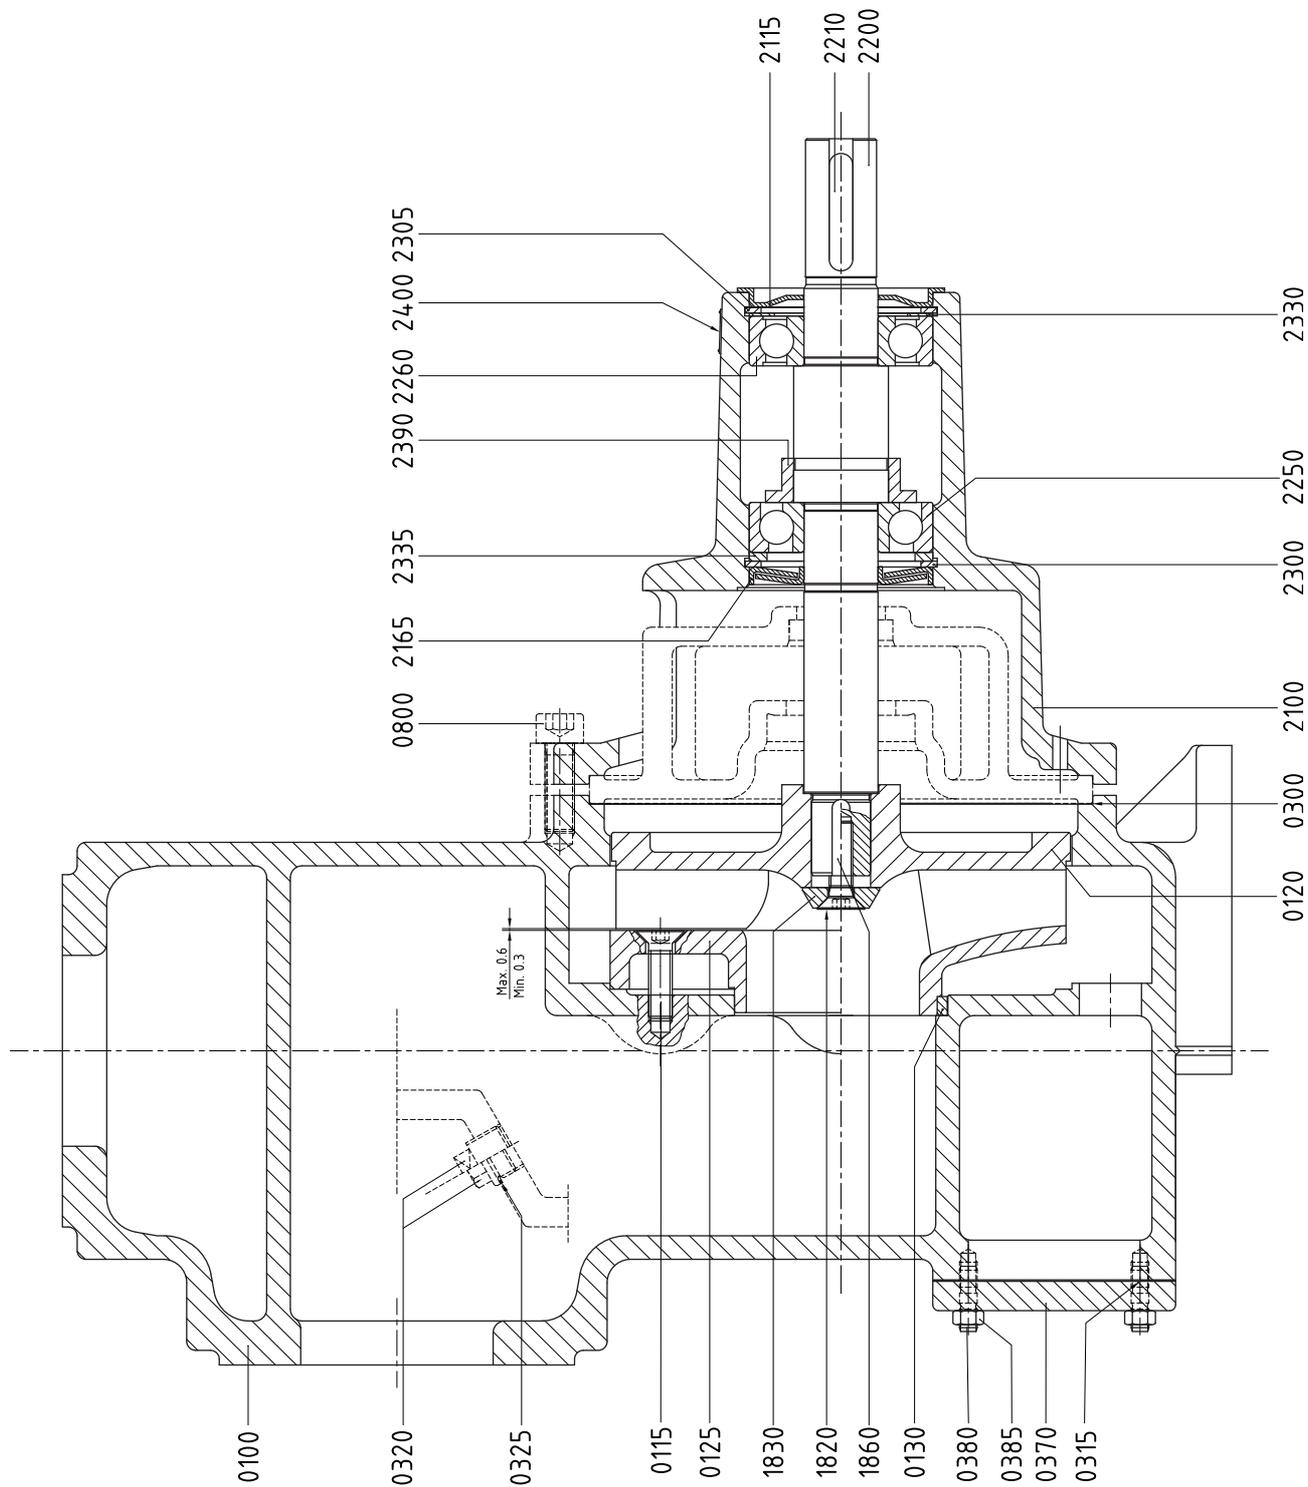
Schnittzeichnung FRE - Lagergruppe 2.
